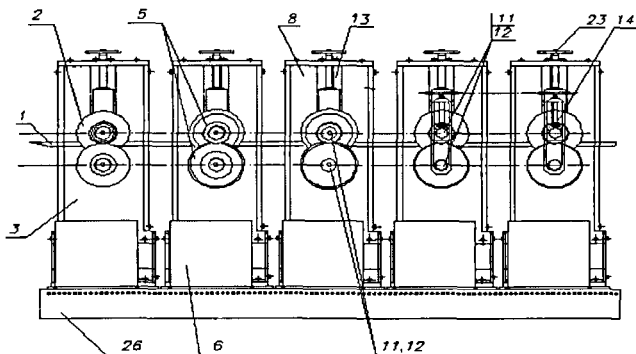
Общий вид волоочно-прокатной установки (ВПУ), вид спереди: 1- плоская листовая заготовка; 2- роликовая пара; 3- рабочая клеть, 5- неприводная роликовая пара, 6,8 (приводная) - рабочая клеть, 9 - вращающаяся роликовая пара, 11, 12 - рабочие валы; 13 - втулки-ползуны, 14- хомуты, 23 – ходовой винт, 26 – направляющие рамы
